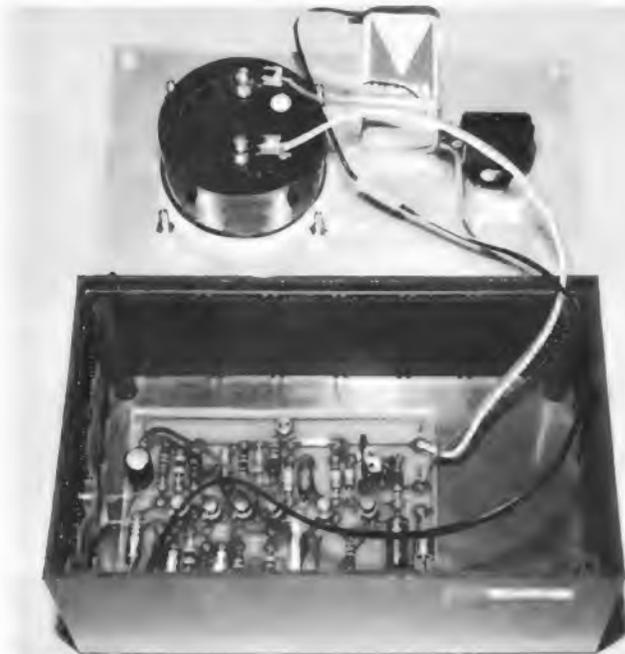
Innenansicht des Gerätes im Teko-Gehäuse P/3
